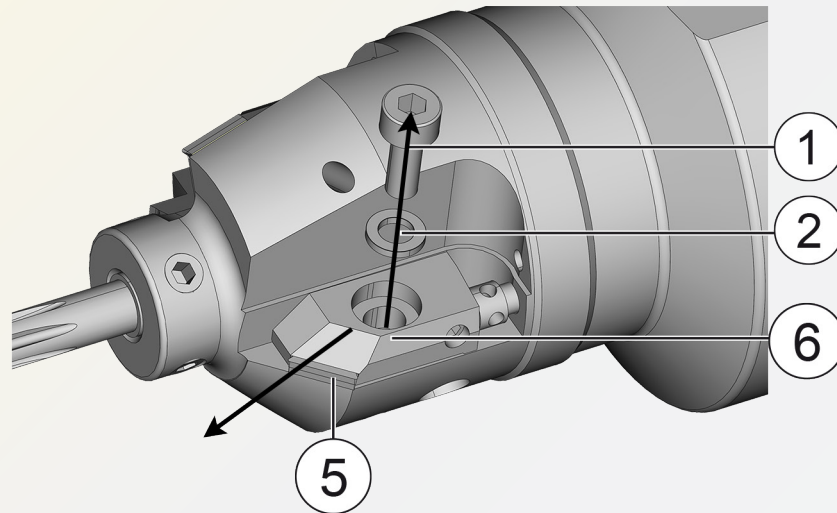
Spannschraube und Unterlegscheibe entfernen
